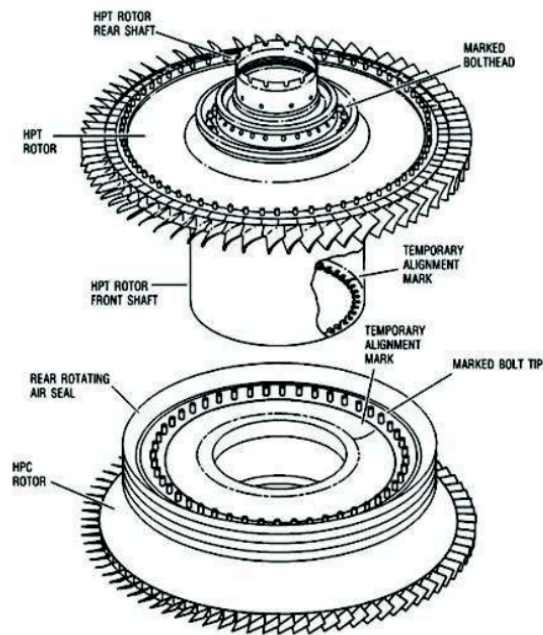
Montagem do *front shaft* da HPT com o CDP Seal, [26]
